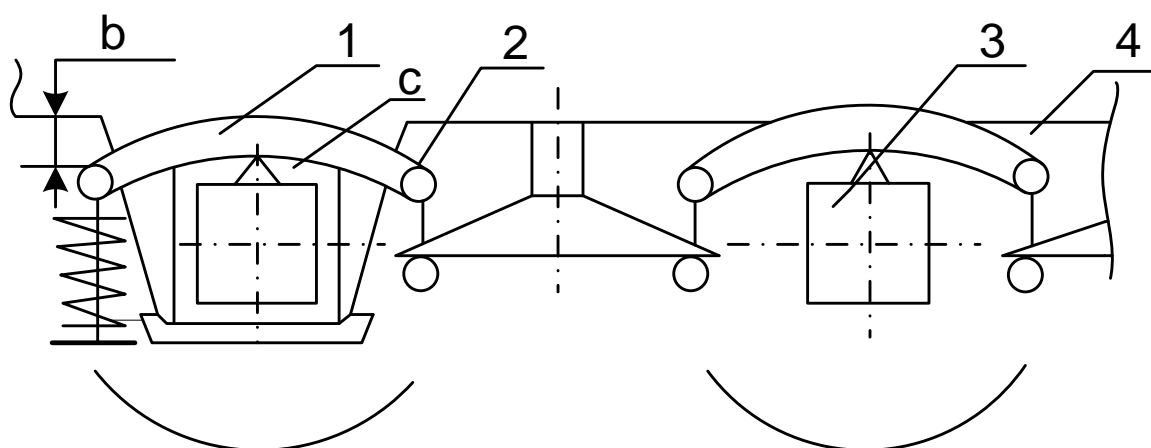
Проверка качества сборки рессорного подвешивания у челюстной тележки: 1 – балансир; 2 – рессорная подвеска; 3 – букса; 4 – рама тележки
